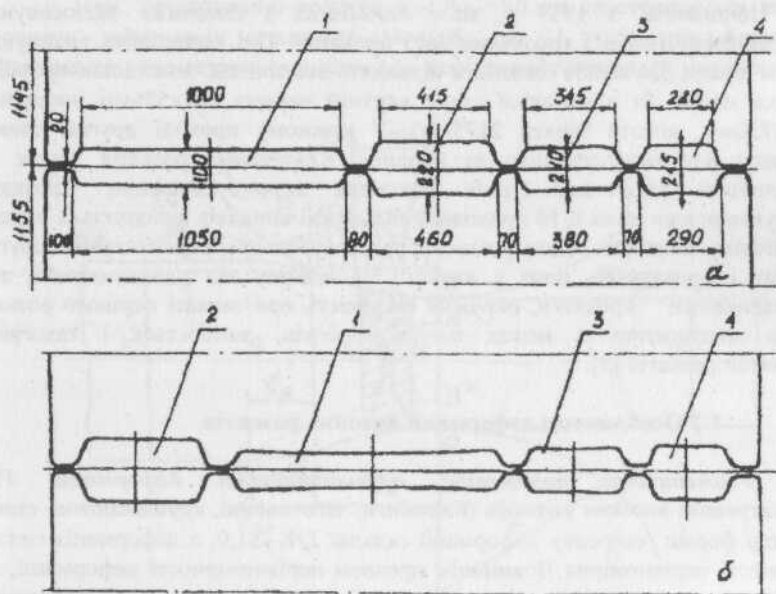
Схеми розташування калібрів: а - гладка бочка з краю валка; б - в середині
